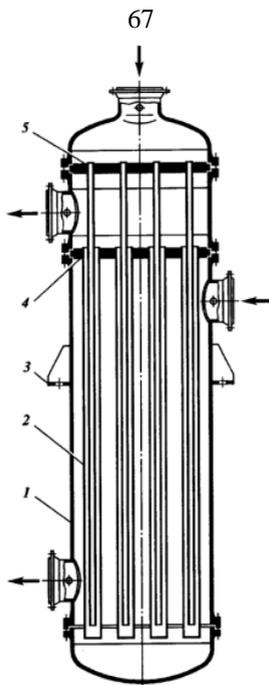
Вертикальный КТТ с двойными трубками (трубками Фильда): 1 –кожух; 2 –наружные теплообменные трубы; 3 –опорные лапы; 4 – трубные решетки; 5 – внутренний пучок теплообменных труб
